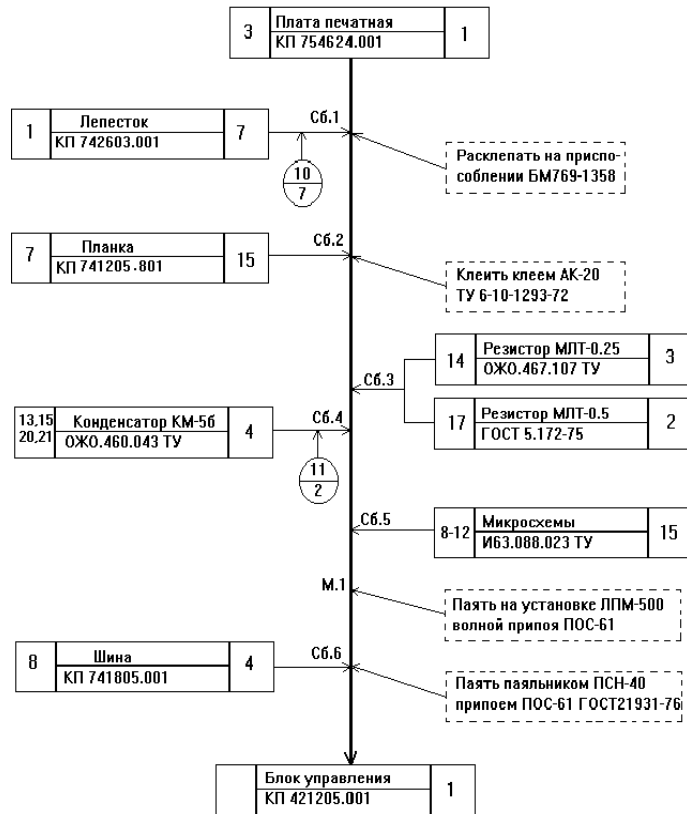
Технологическая схема сборки блока с базовой деталью
